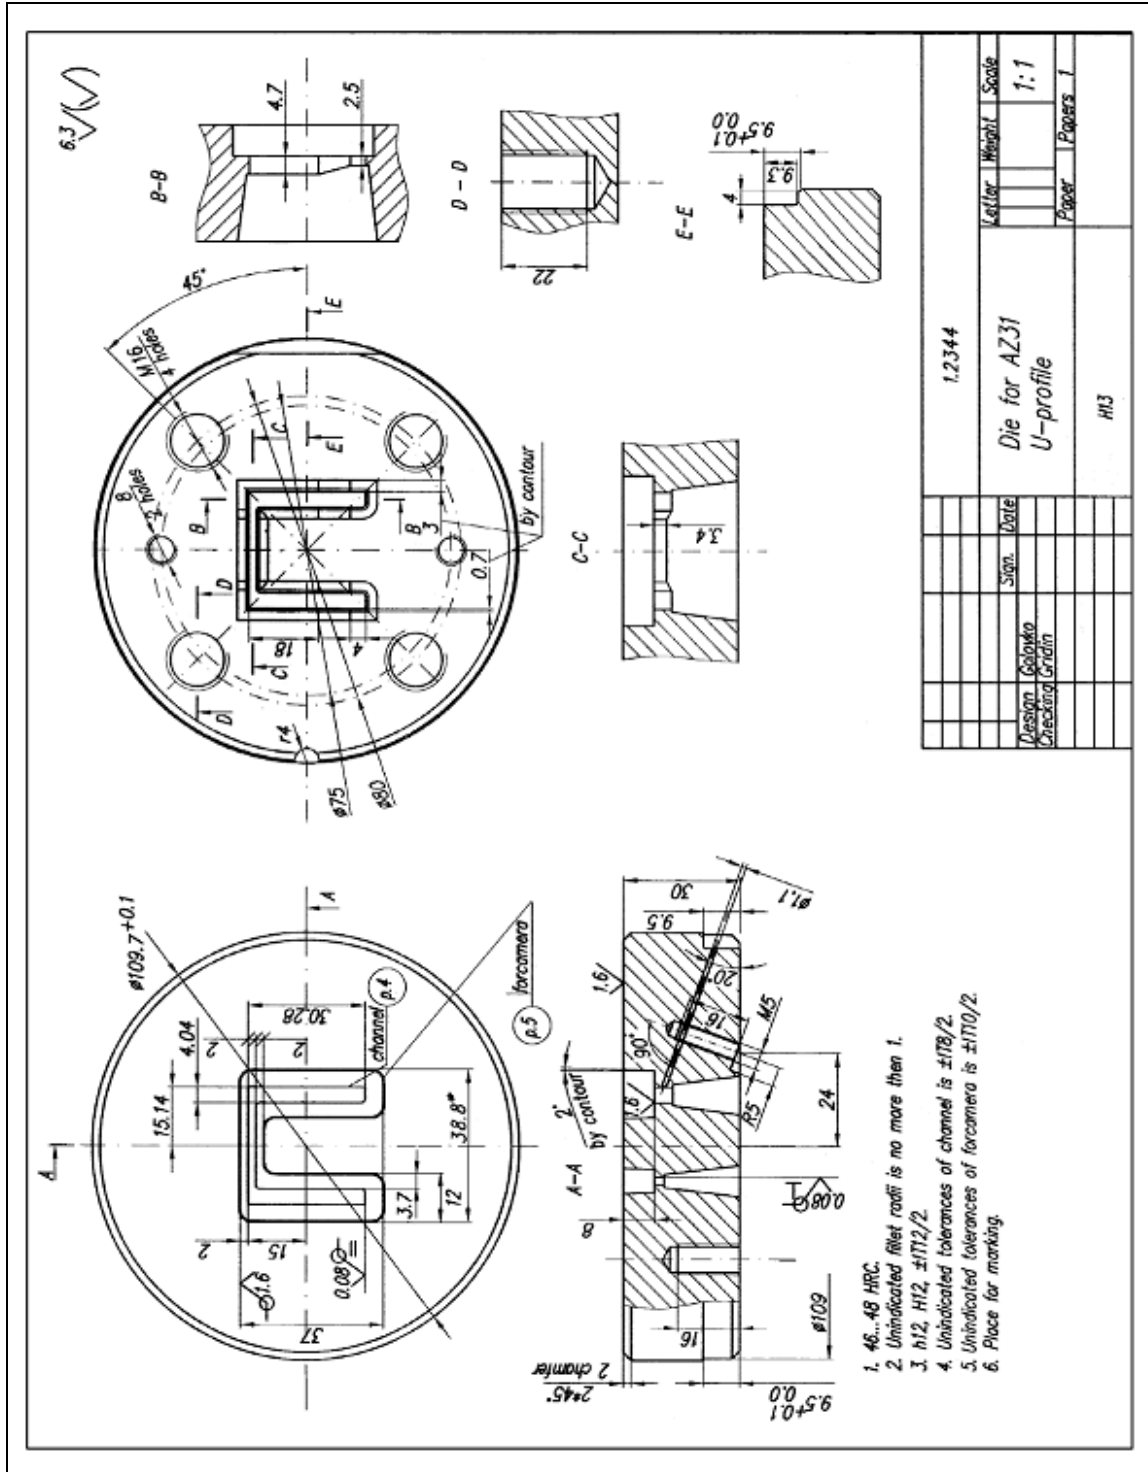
Zeichnung des Werkzeuges mit Vorkammer
